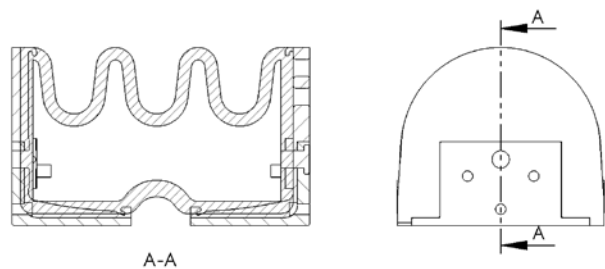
Schnitt durch die Seitenansicht des Biegeaktors
